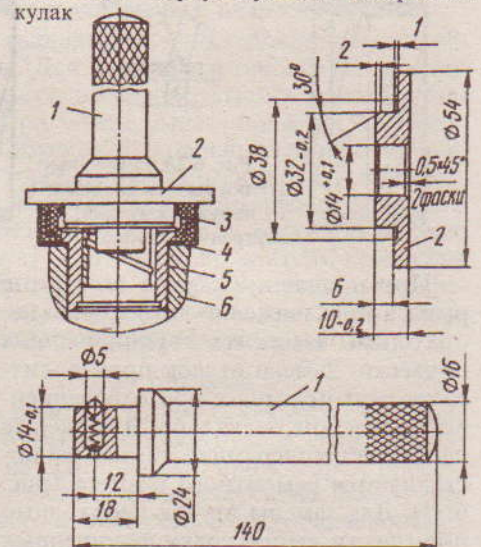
Запрессовка манжеты шкворня: 1 - ручка; 2 - оправка; 3 - манжета; 4 - обойма манжеты; 5 - корпус втулки; 6 - поворотный кулак
